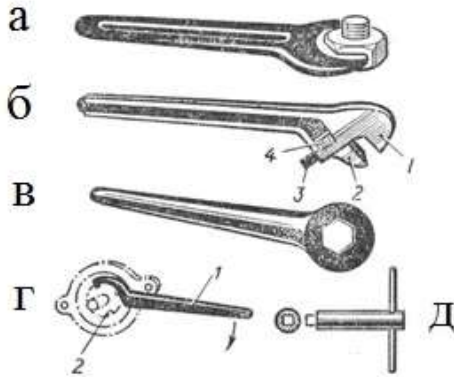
Гайкові ключі: а – односторонній відкритий; б – розсувний з черв'ячним гвинтом (1 – нерухома частина, 2 – рухома частина, 3 – зубчаста рейка, 4 – черв'ячний гвинт); в – накидний (закритий); г – радіусний – для круглих гайок (1 – штир ключа, 2 – паз); д – торцевий.
